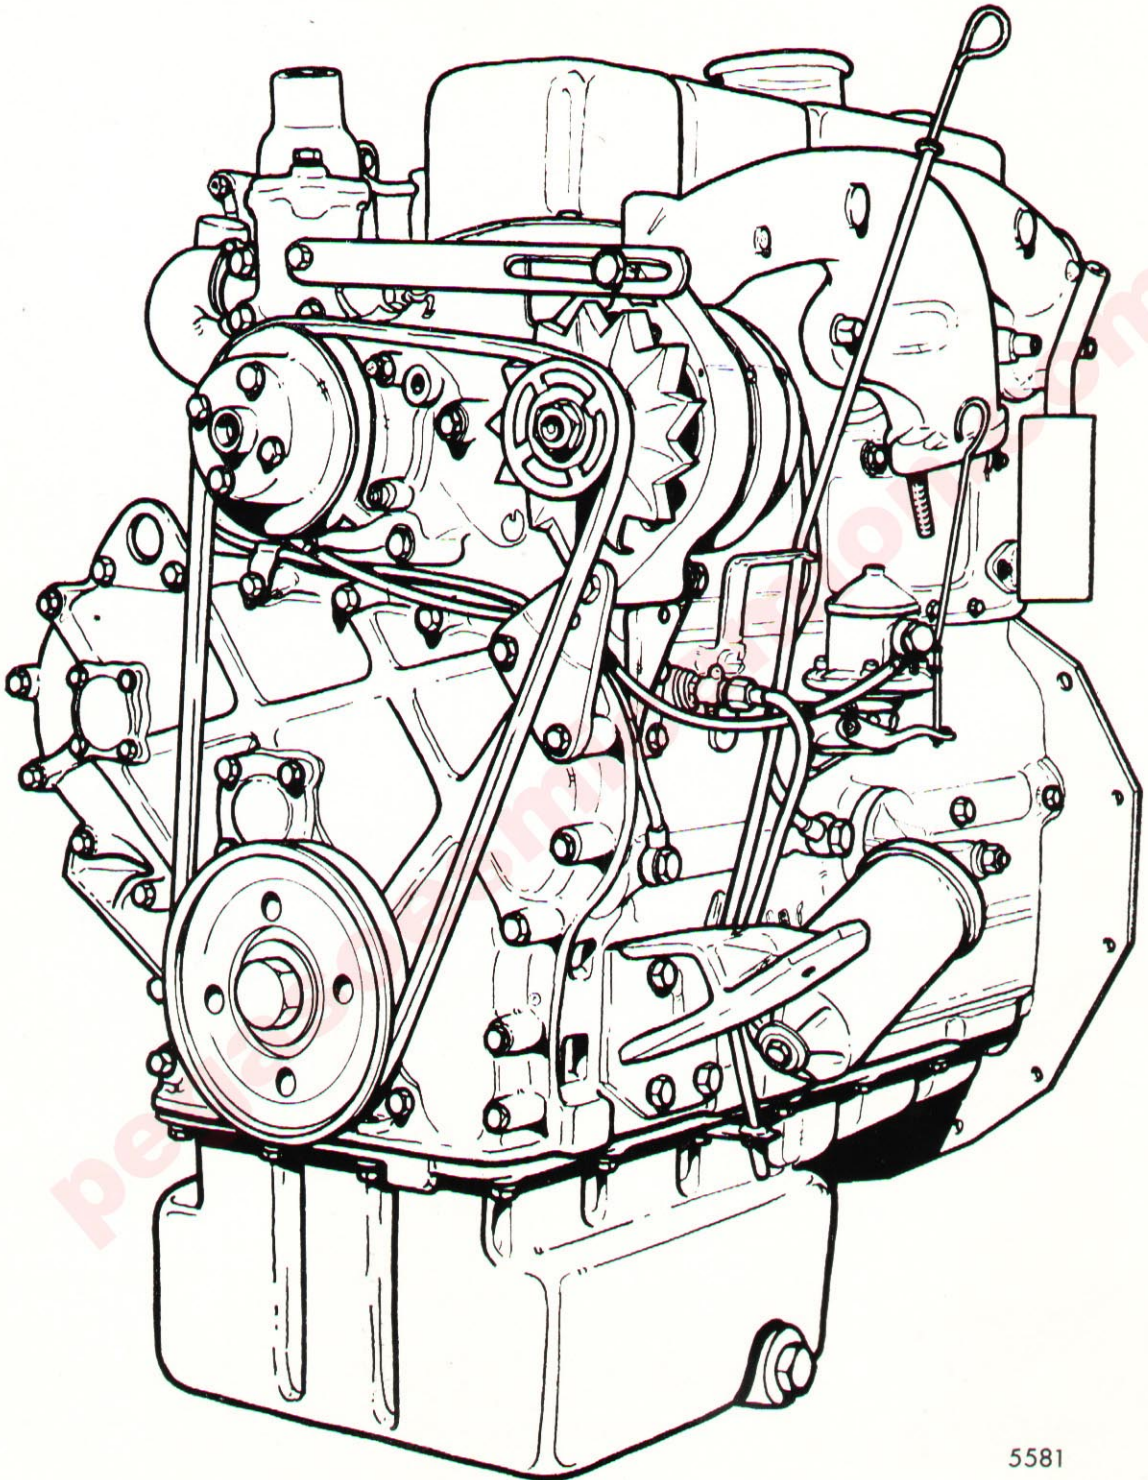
Motor tipo 9700 (3.8) con dínamo. Lado izquierdo.
